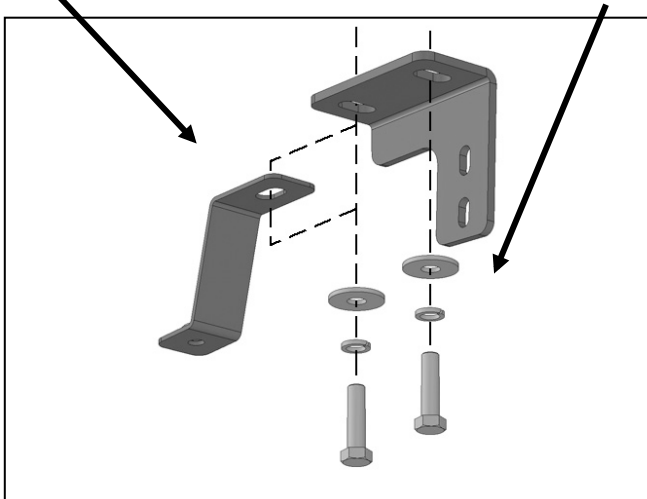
Para modelos sin ganchos de remolque, corte aberturas en la cubierta de plástico inferior para despejar los soportes
